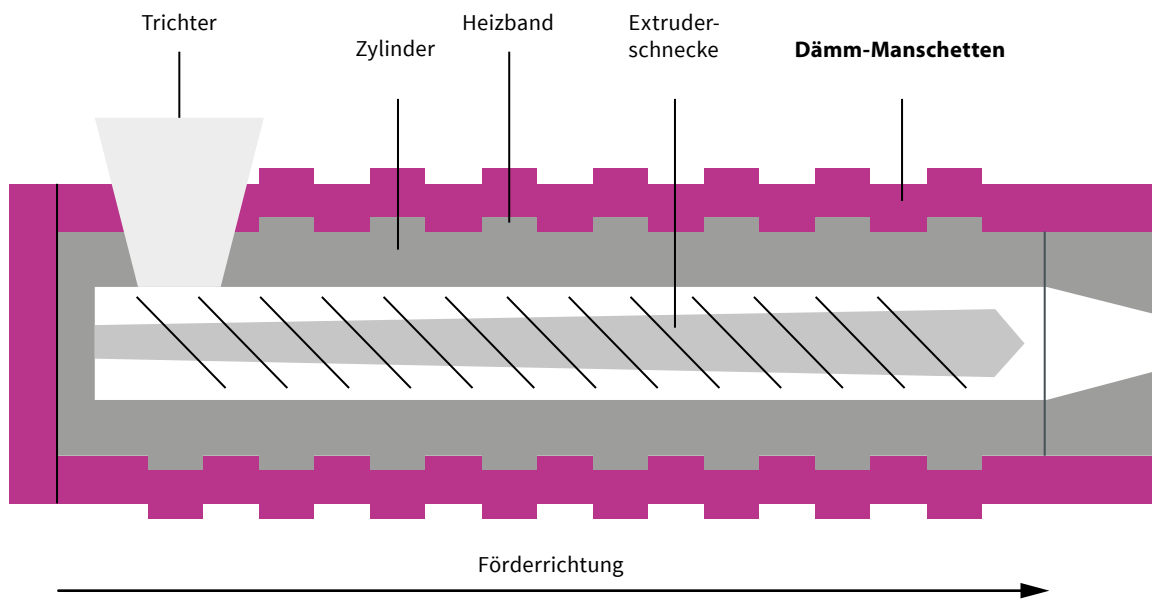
Wärmedämmung an einer Extrusionsmaschine. Quelle: dena
